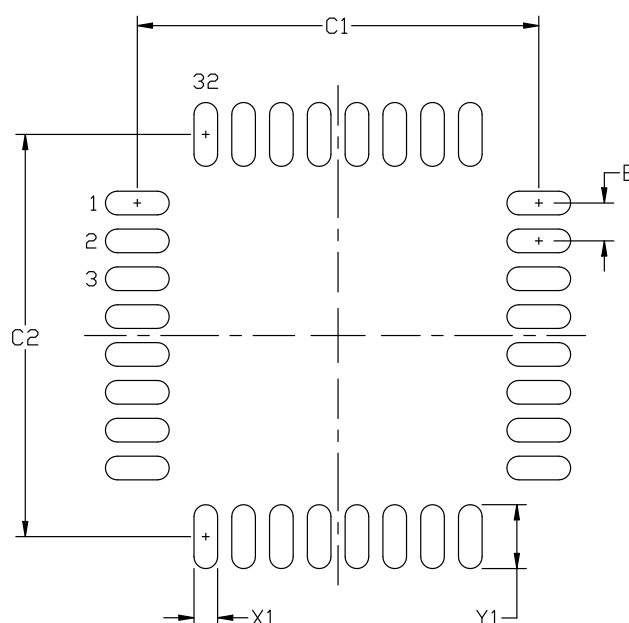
QFP32 PCB 焊盘布局图
